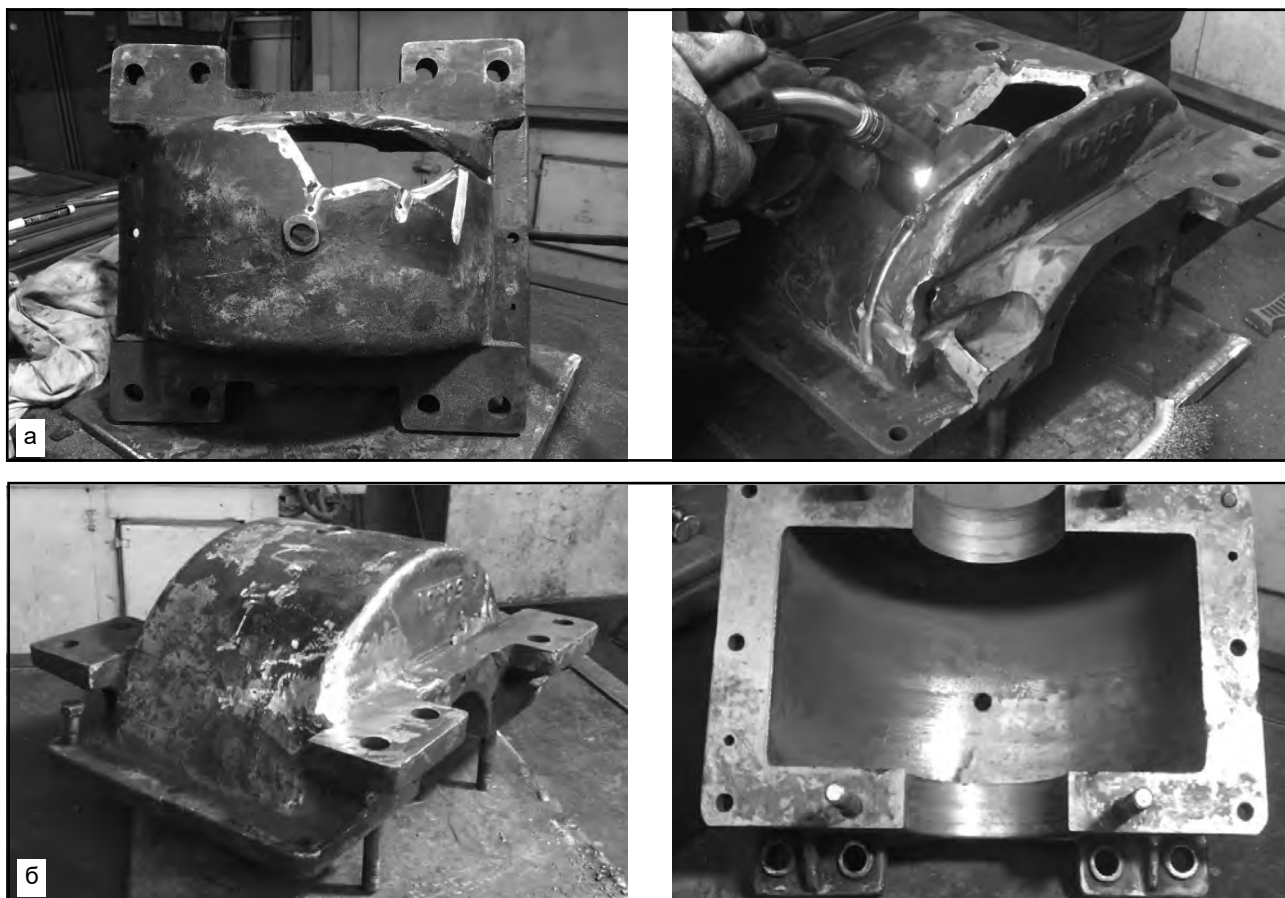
Аргодуговая (TIG 141) и полуавтоматическая сварка (MAG 135). Ремонт чугунного корпуса редуктора передвижения крана. Док 152 Пр.Б. Сварка чугуна, январь 2019 г.: а) сварочные работы - до ремонта, б) после ремонта
